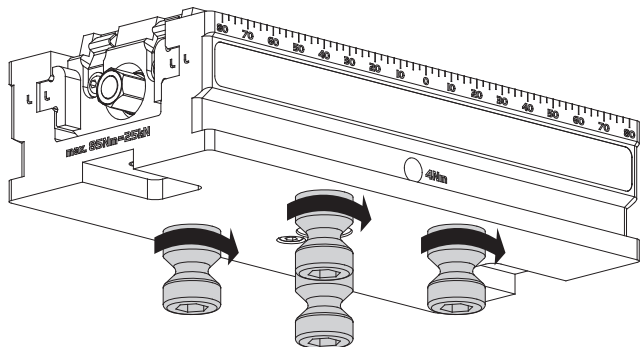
Menghină cu fixare centrică pentru Quick-Point
